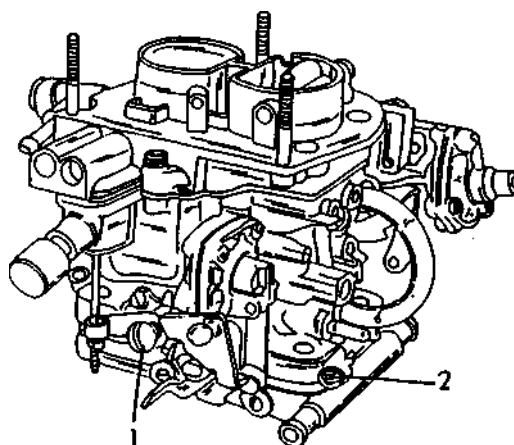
Seřizovačí šroub volnoběžných otáček -1- a obsahu CO -2- u karburátoru Solex
